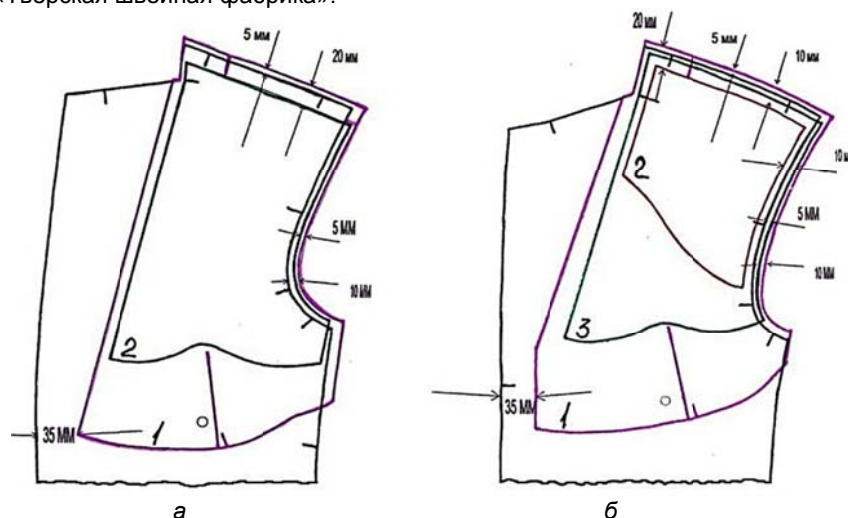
Схема сборки переда пиджака с БП: а – двухслойным; б – трехслойным
